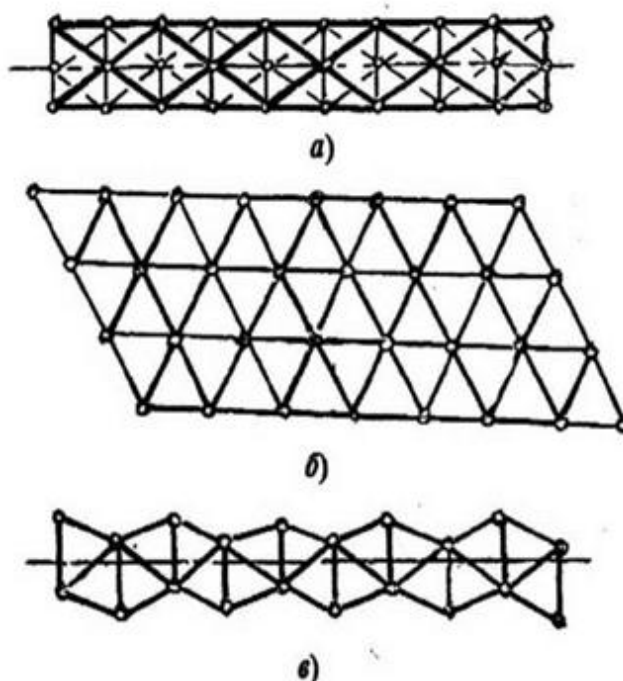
Ствол винтового ротора станка для отделочно-зачистной и упрочняющей обработки деталей (а- вид спереди, б-развертка боковой поверхности, в-вид сбоку)
